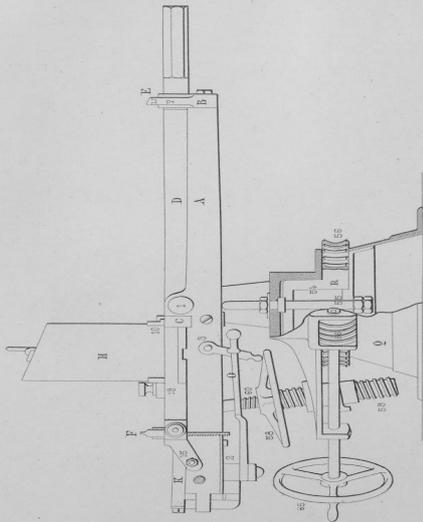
Mécanisme, le coup parti. Echelle 1/6
